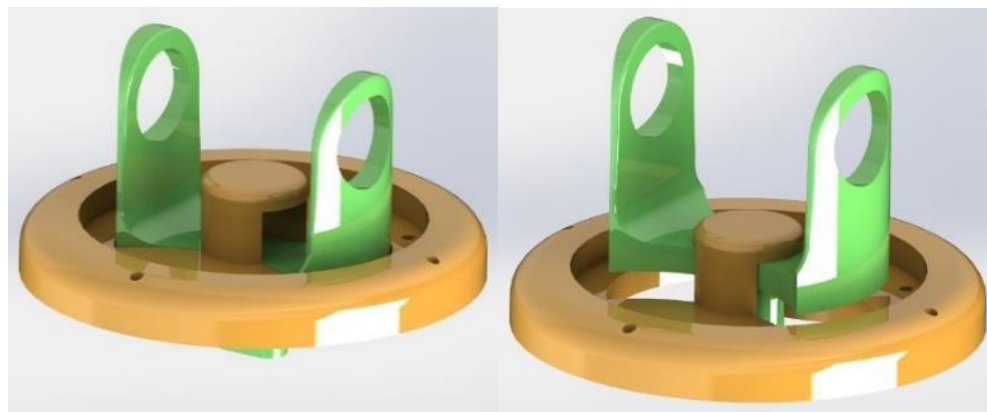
a) Montaje de junta universal. b) Vista explosionada
